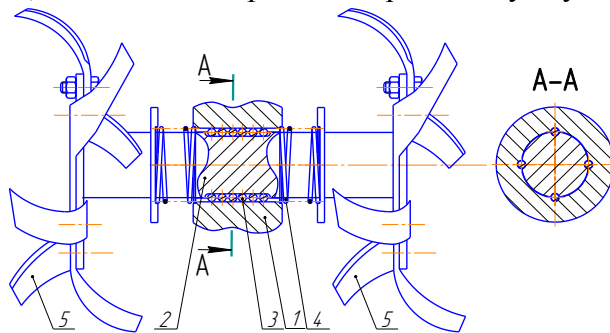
Принципова схема секції фрезерного культиватора для міжрядного обробітку ґрунту: 1 – опора, 2 – вал, 3 – кульки, 4 – пружина, 5 – фреза.
